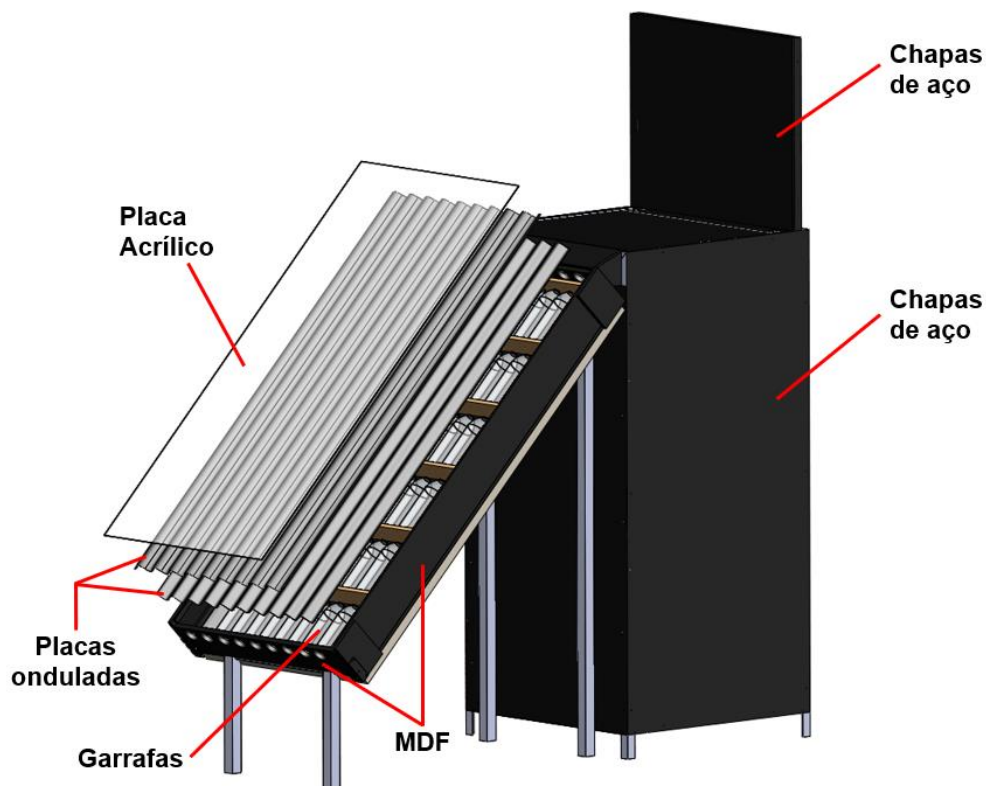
Secador solar com vista explodida do coletor solar [1]
